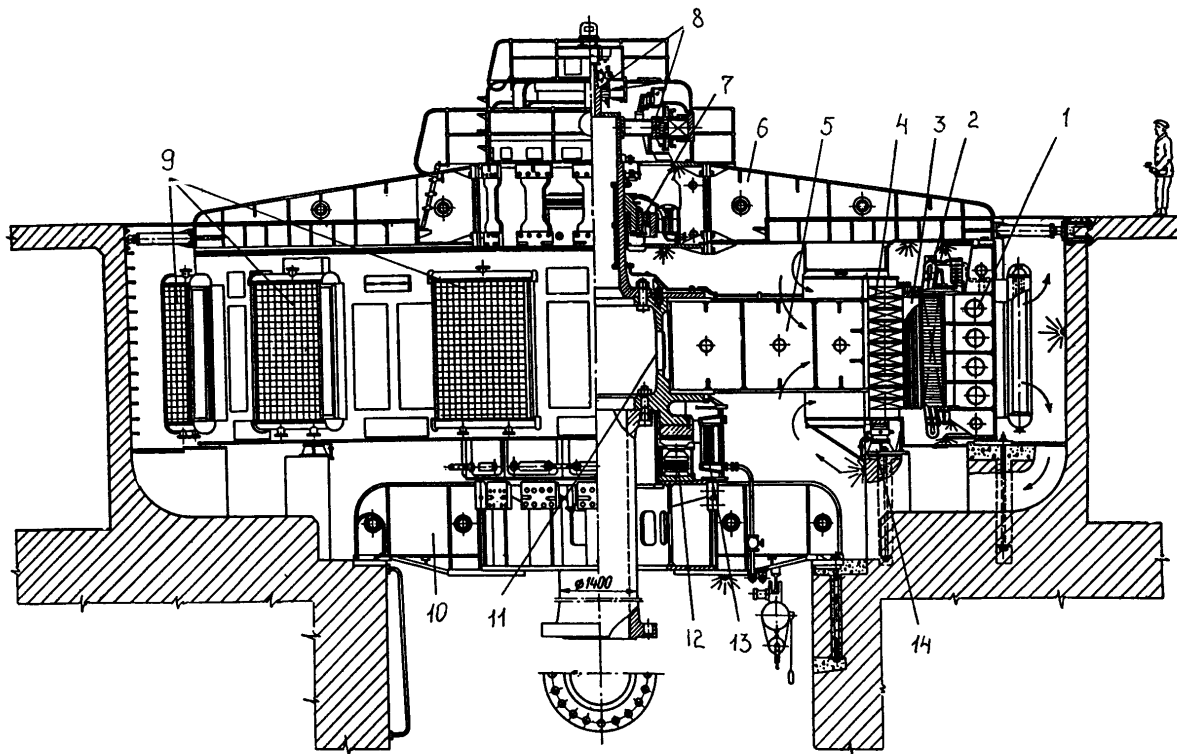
Гидрогенератор ГЭС Кариба-2 (Замбия) зонтичного типа с опорой на нижнюю крестовину ($P = 150$ МВт; $\cos\phi = 0,9$; $f = 50$ Гц; $n = 100$ об/мин): 1 — корпус статора; 2 — обмотка статора; 3 — полюс ротора; 4 — обод (активная сталь) ротора; 5 — остов ротора (спицы); 6 — верхняя крестовина; 7 — направляющий подшипник; 8 — система возбуждения; 9 — воздухоохладители; 10 — нижняя крестовина; 11 — втулка ротора; 12 — сильфонный (гидравлический) подпятник; 13 — маслоохладители подпятника; 14 — тормоз
